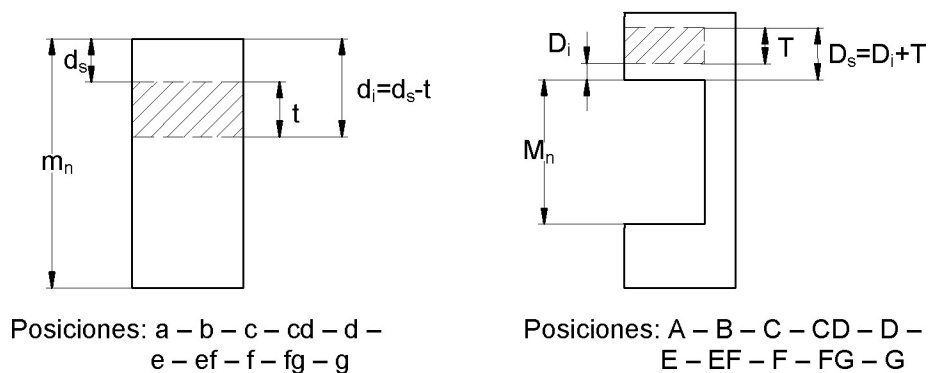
Posiciones de ejes más pequeños que la medida nominal (izquierda) y posiciones de agujeros más grandes que la medida nominal (derecha)
